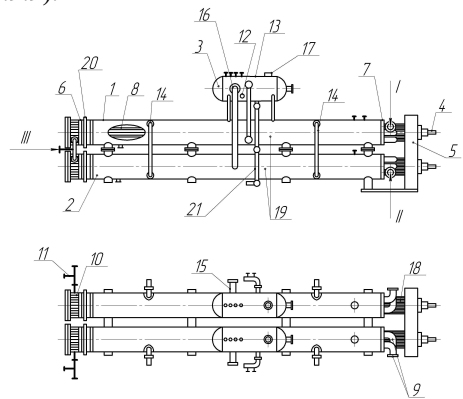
Кожухотрубний кристалізатор зі скребокними пристроями:
